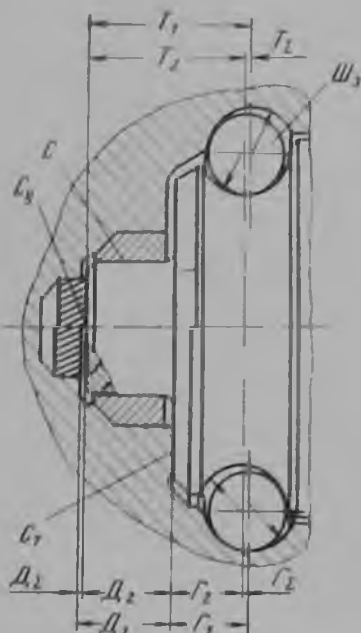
Схема зазоров в опоре с подшипниками скольжения.
